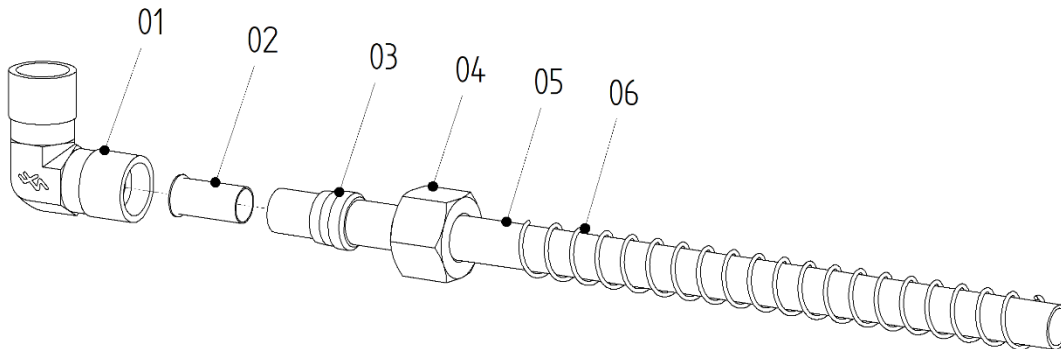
Anschlussleitung mit Winkel-Einschraubverschraubung
